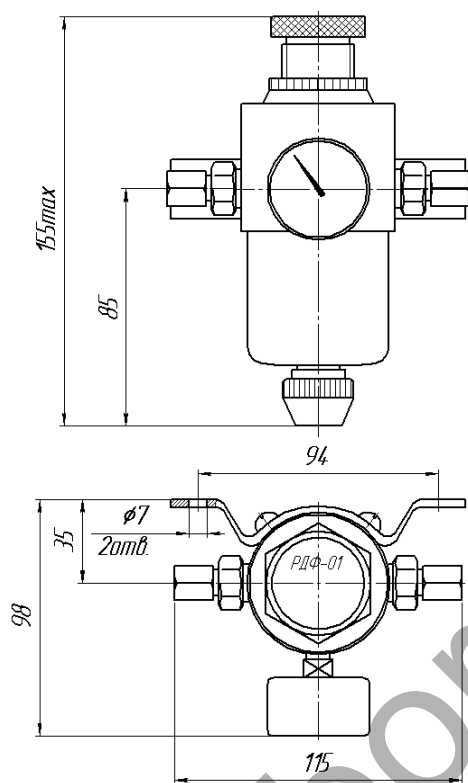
Габаритные и установочные размеры редуктора РДФ-01
